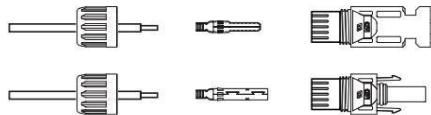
Desmontaje de la tuerca de la tapa del conector
